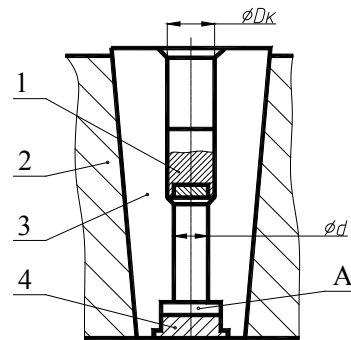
Эскиз матричного узла оснастки для изготовления стержневого инструмента по способу [6]: 1 – заготовка; 2 – обойма; 3 – полуматрица; 4 – вставка
